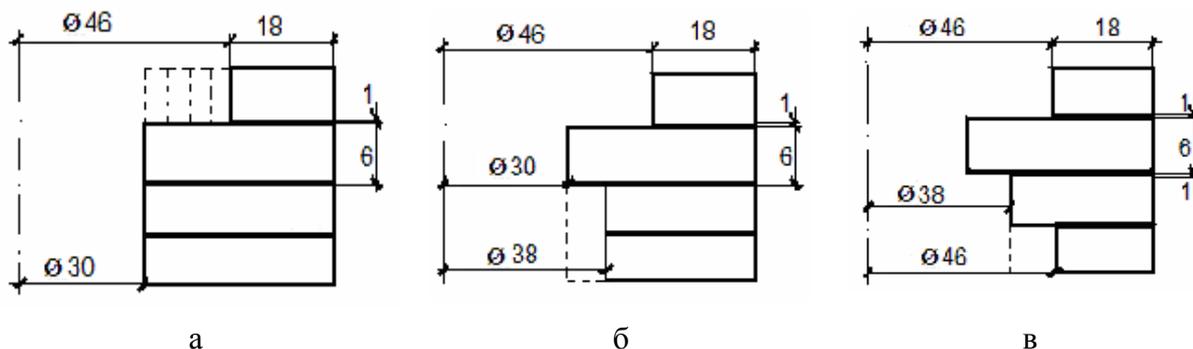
Схемы подбора геометрических размеров спирали индуктора
